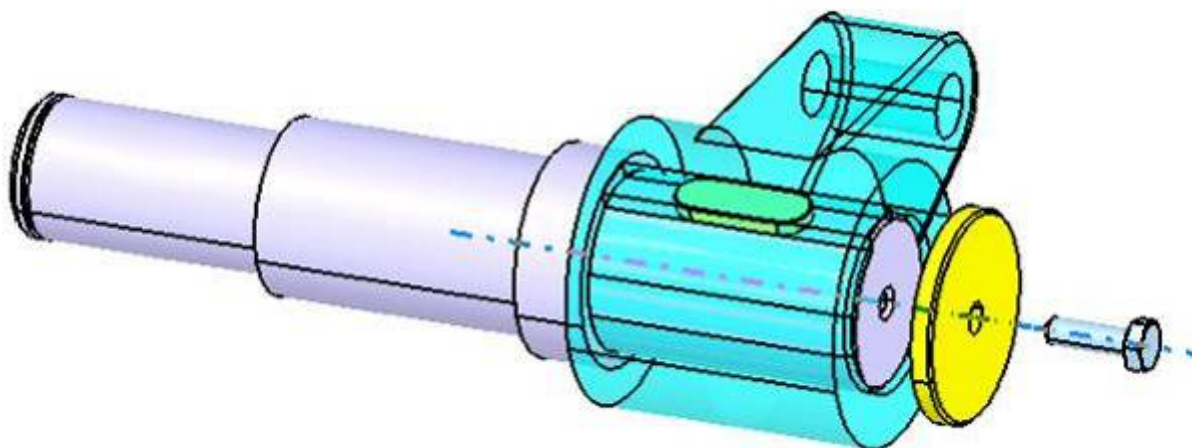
Fixarea axială a bucșei cu bridă în ansamblu
